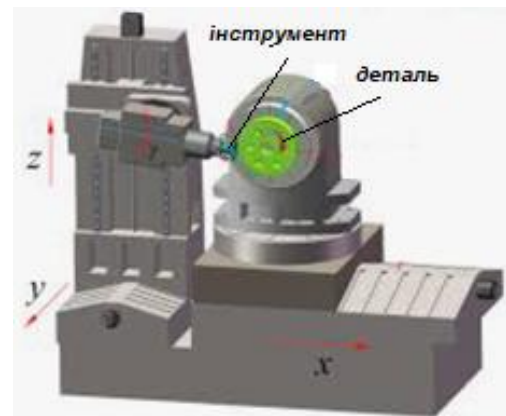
Загальний вид спеціалізованого зубонарізного верстата з ЧПК для процесу Power skiving
